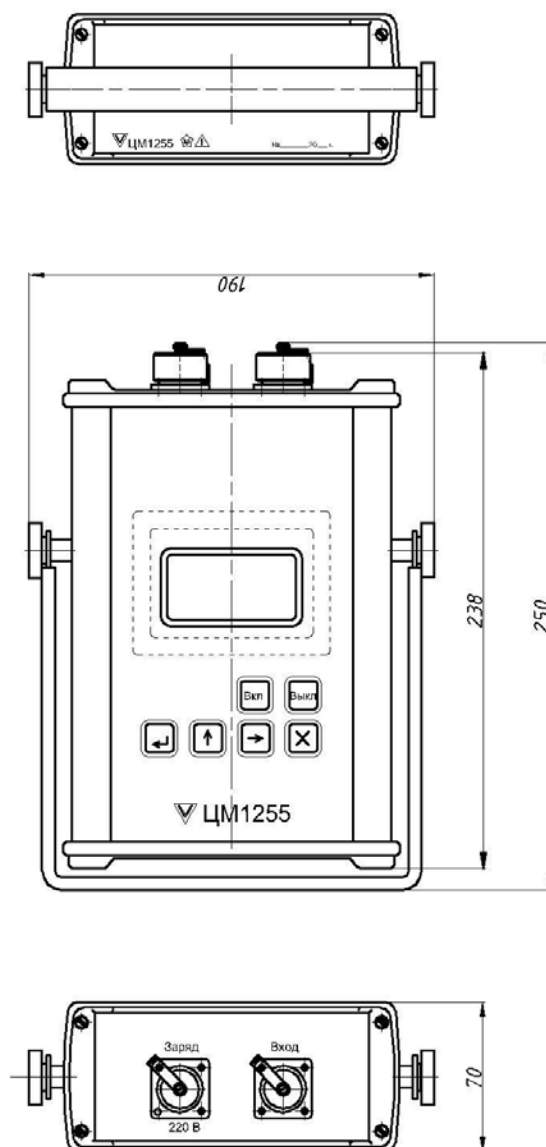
Внешний вид и габаритные размеры ЦМ1255
